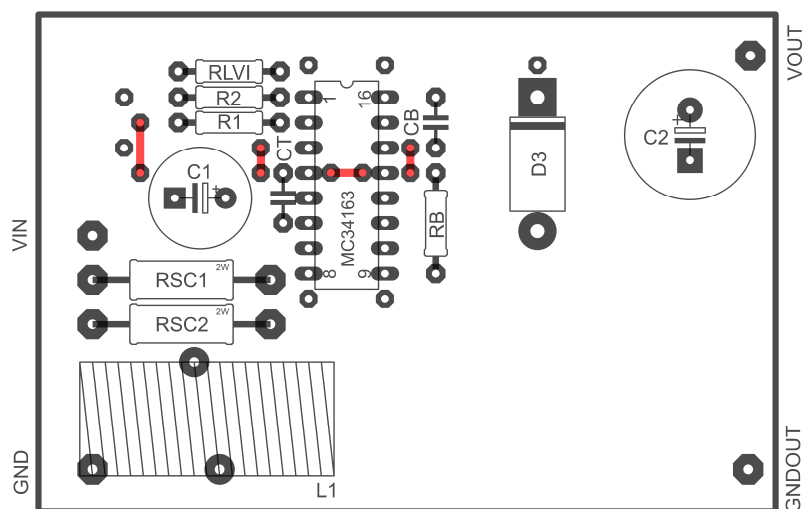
Univerzální schéma zapojení pro všechny tři typy měničů
